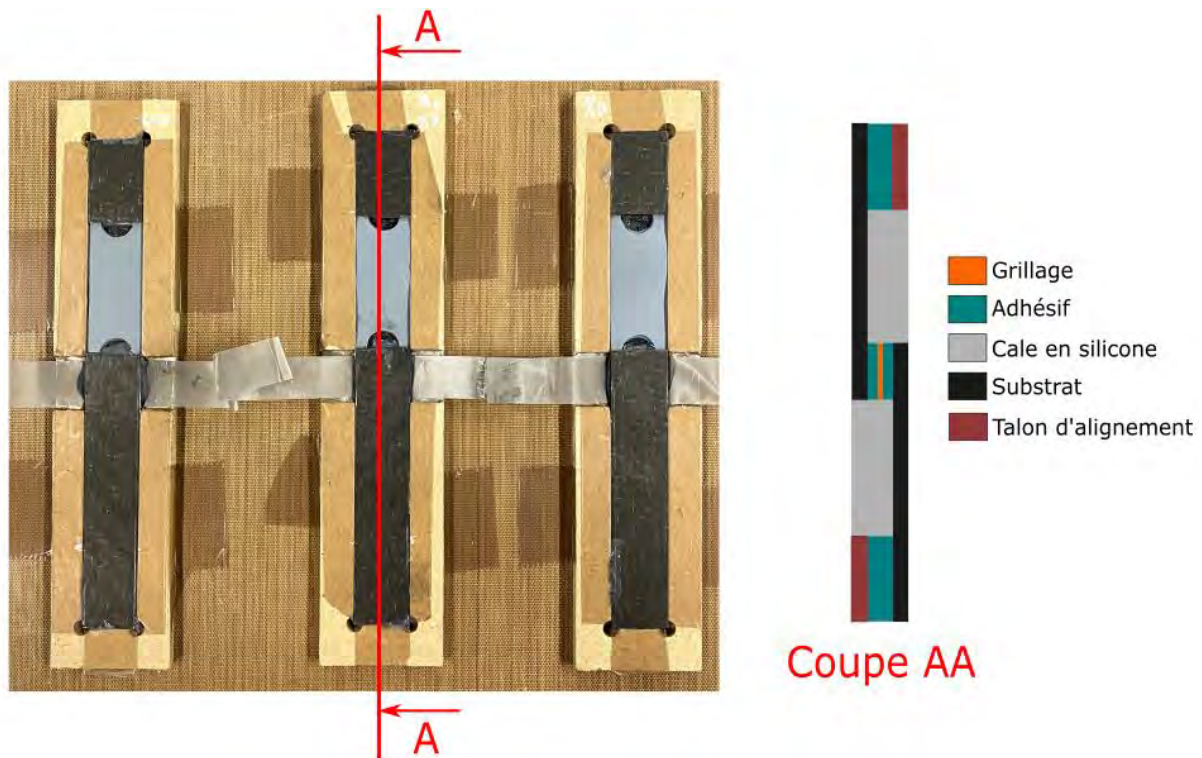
Moule de fabrication des éprouvettes du type SLJ avec les éprouvettes installées (à gauche) et une vue coupée du placement des éprouvettes dans le moule pour fixer les épaisseurs (à droite).
